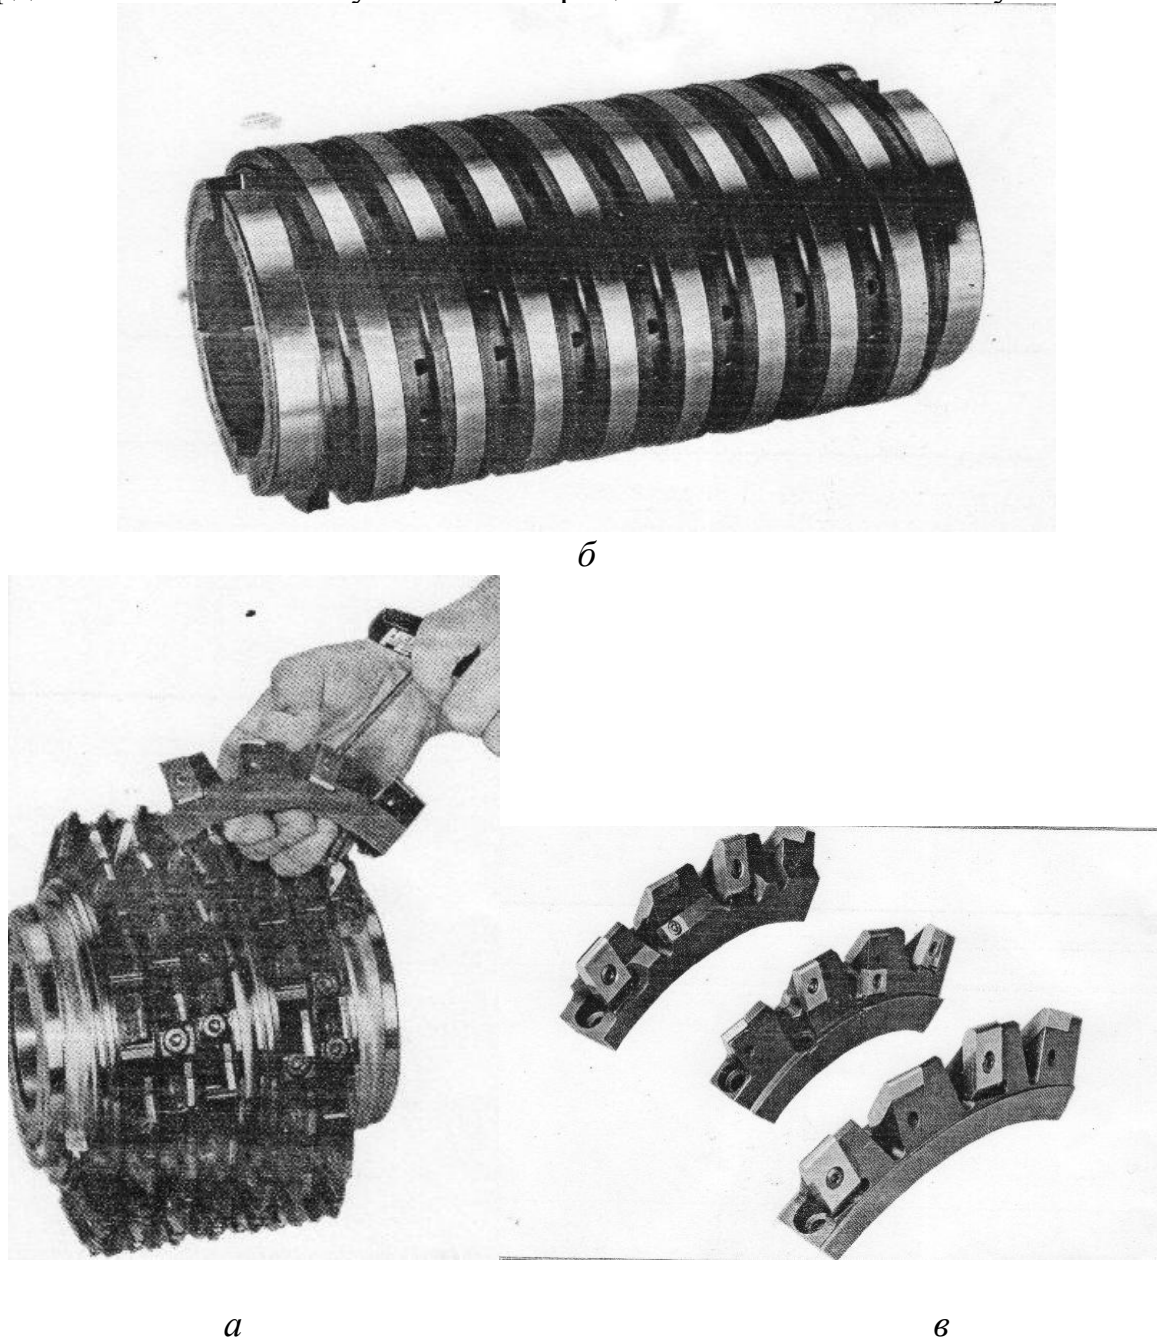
Червячная фреза сборной конструкции фирмы “Fette” (ФРГ) $m=12\text{мм}$: а – фреза в сборе; б – корпус фрезы с винтовой канавкой; в – зубчатые сектора с неперетачиваемыми поворотными пластинками.
